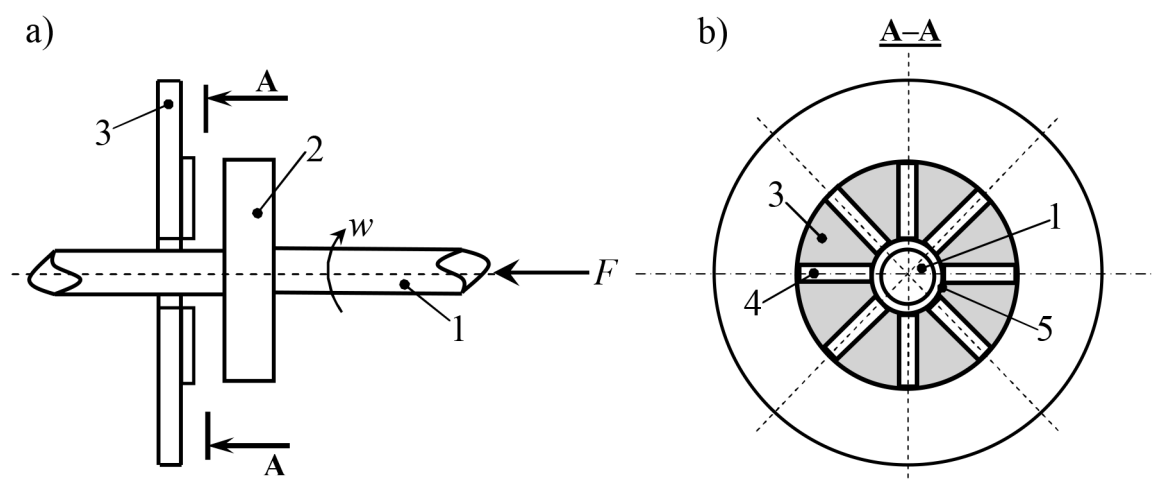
Схема упорного гидродинамического подшипника (а) вид сбоку; б) разрез АА): 1 – ротор; 2 – пята; 3 – УП; 4 – осевая канавка; 5 – кольцевая канавка
